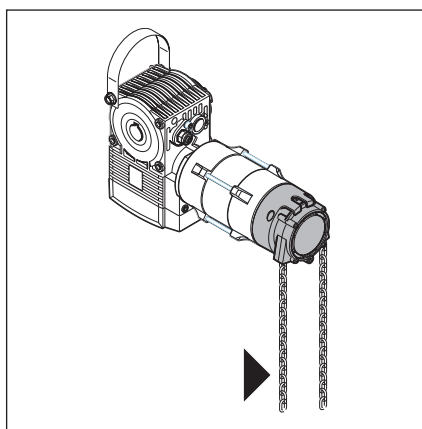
Фланцевый привод с цепной ручной аварийной деблокировкой
